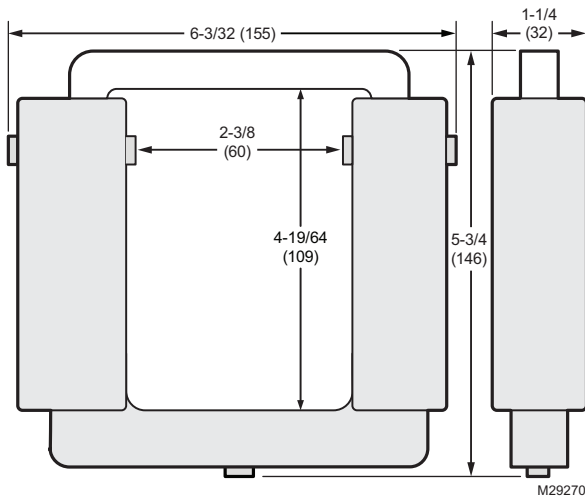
Dimensions du capteur de courant 800 et 1600 A en po (mm).
